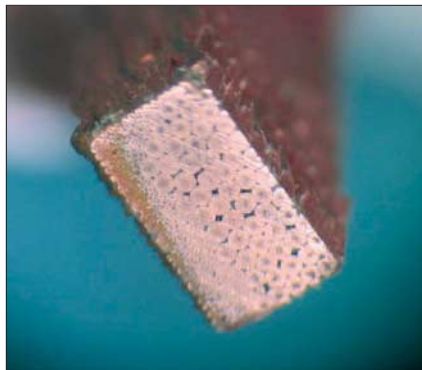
Schliffbild einer US-Schweißverbindung
